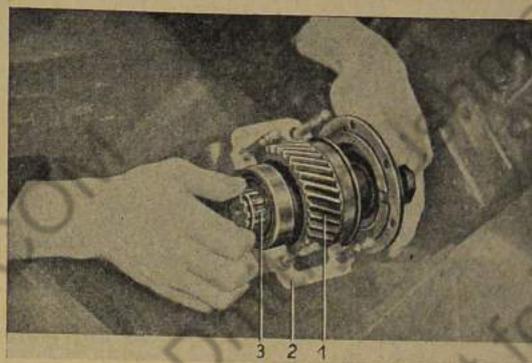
Antriebsrad mit Flanschswelle aus dem Zwischenradgehäuse herausheben
